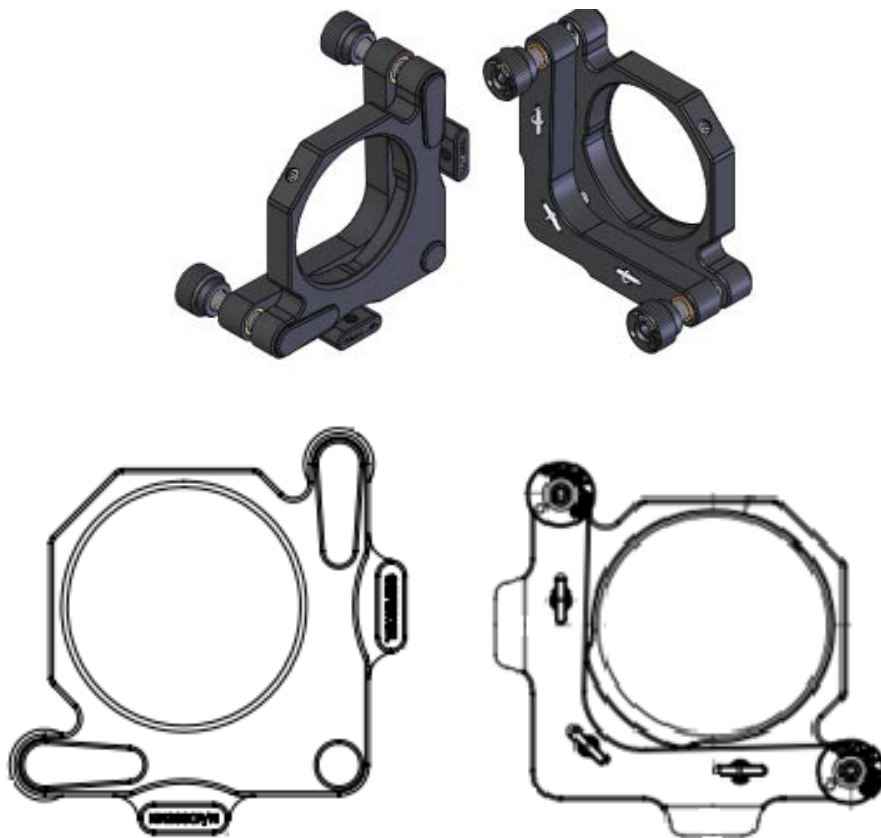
Ескіз механічної частини пристрою для юстування нерухомого дзеркала
